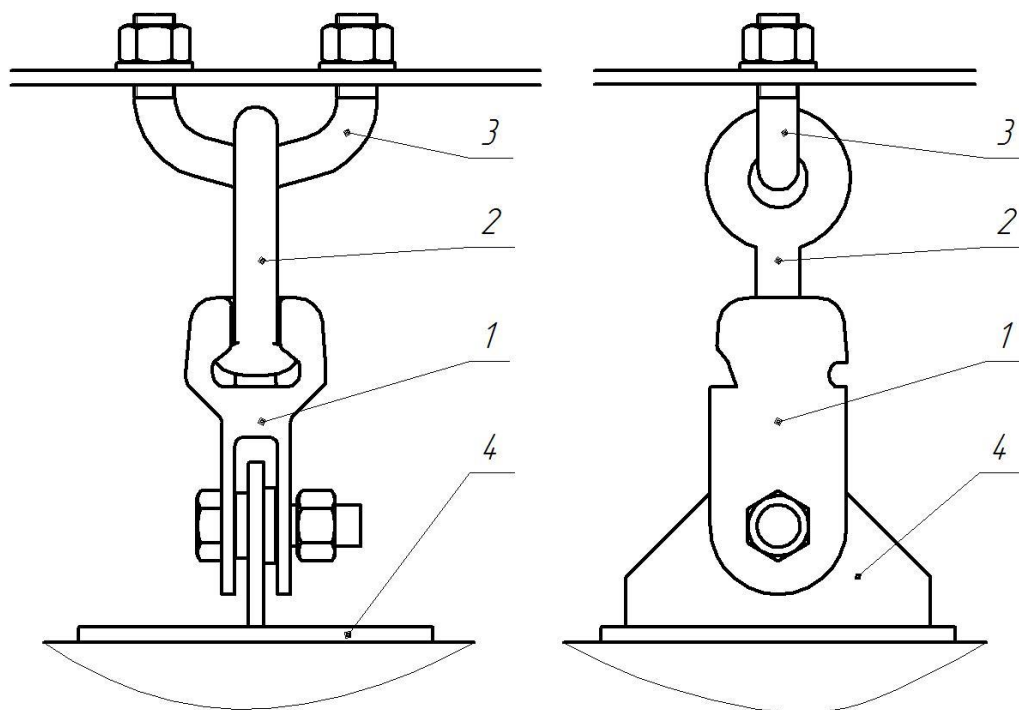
А – крепление измерительного компонента устройства I-TOR-35 на опоре электропередачи или портале.
